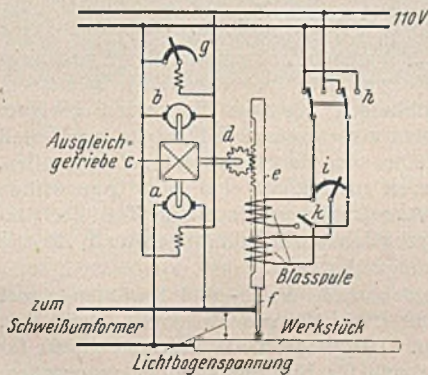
Getriebe einer selbsttätigen Kohlelichtbogenschweißeinrichtung der Siemens-Schuckertwerke AG.
